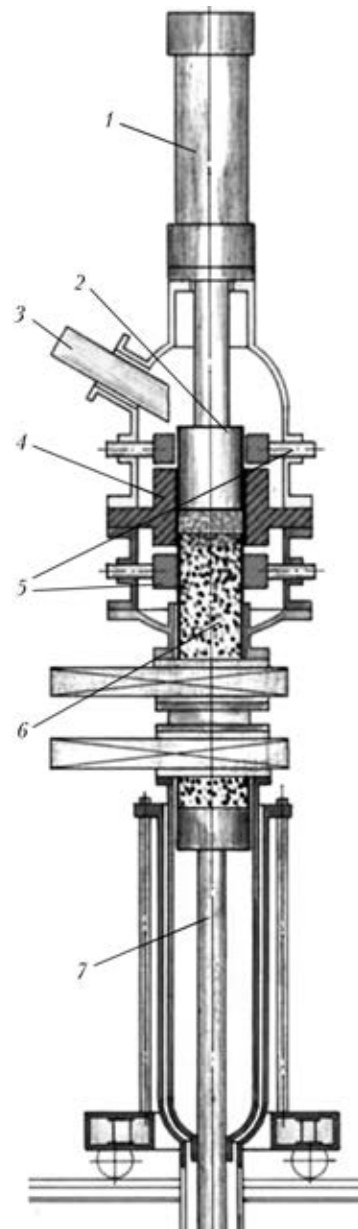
Схема установки для компактирования: 1 – гидроцилиндр; 2 – пуансон; 3 – лоток для подачи стружки; 4 – матрица; 5 – токоподводы; 6 – скомпактированная заготовка; 7 – шток
